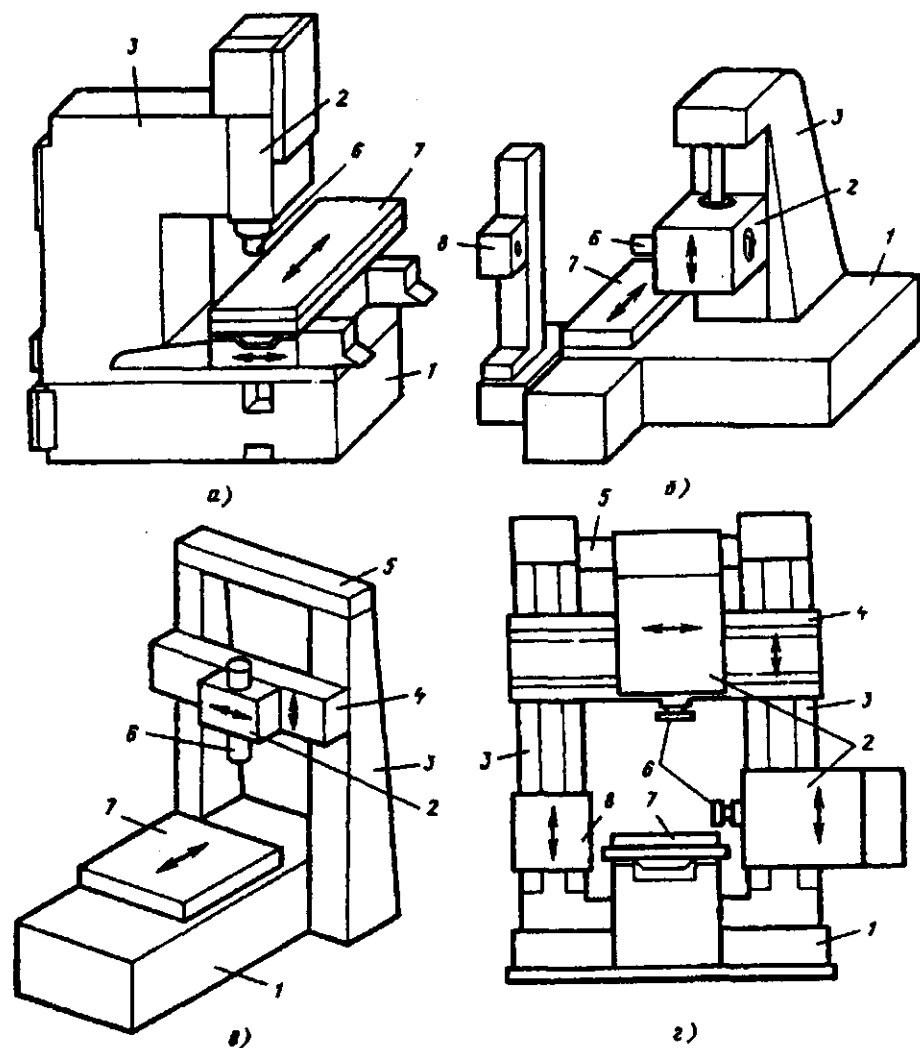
Типовые компоновки КРС: 1 – станина; 2 – шпиндельная бабка; 3 – стойка; 4 – траверса; 5 – поперечина; 6 – шпиндель; 7 – стол; 8 – люнет
